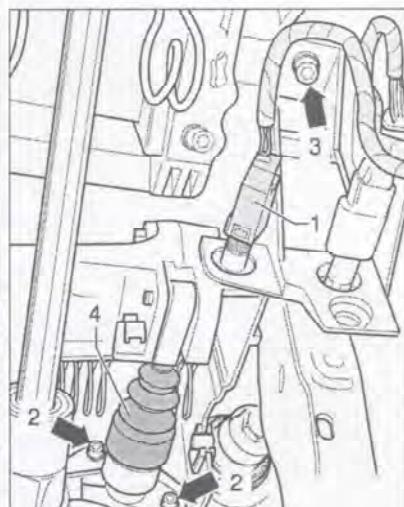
Будьте осторожны: не выдавите датчик педали сцепления (стрелка) из держателя. Отверните болты (стрелки 2) крепления главного цилиндра сцепления (4). Отверните болт (3) кронштейна педального узла.
